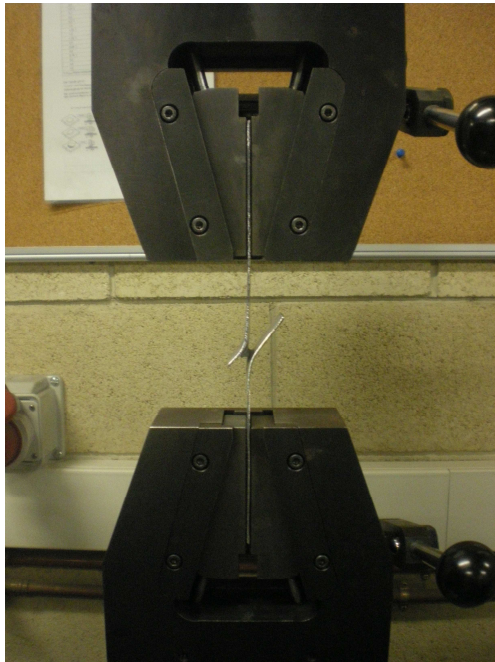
y 4 Detalle estado final de probeta punto ok tras ensayo de tracción
